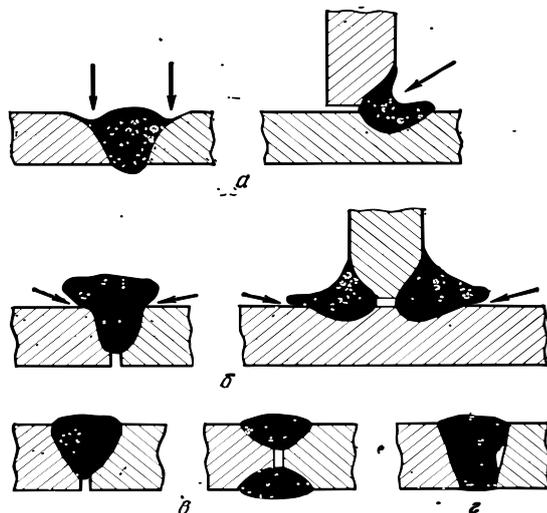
Дефекты при сварке плавлением: а — подрез; б — наплыв; в — непровар по толщине; г - непровар по кромке шва.
